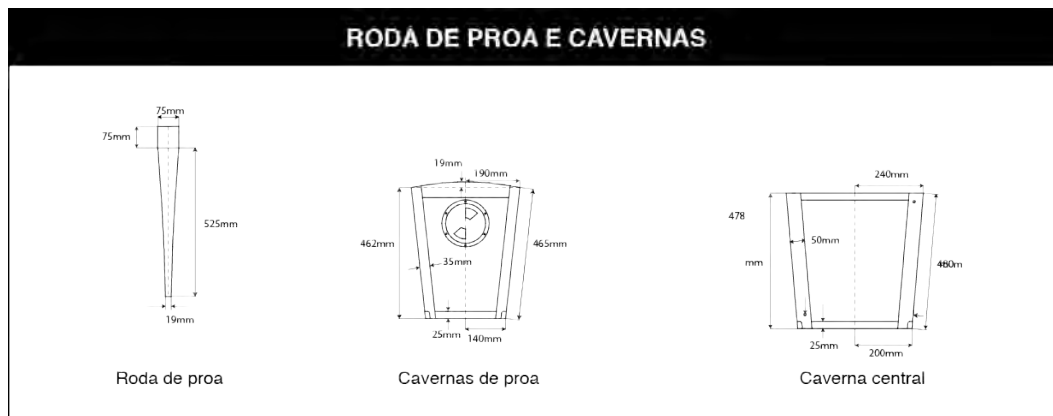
Desenho técnico das cavernas e rodas de proa.
